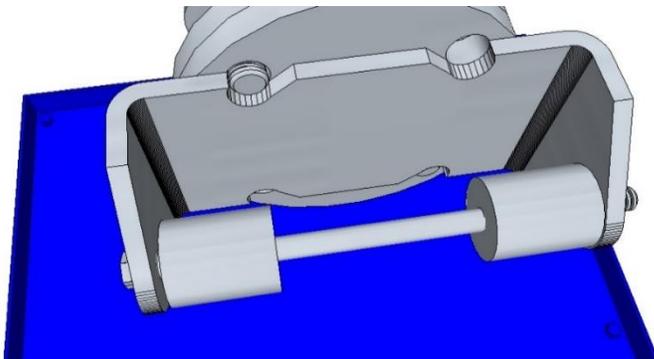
Bujes de relleno y tornillo para soporte del motor en 3D, diseño del creador con fines ilustrativos.
